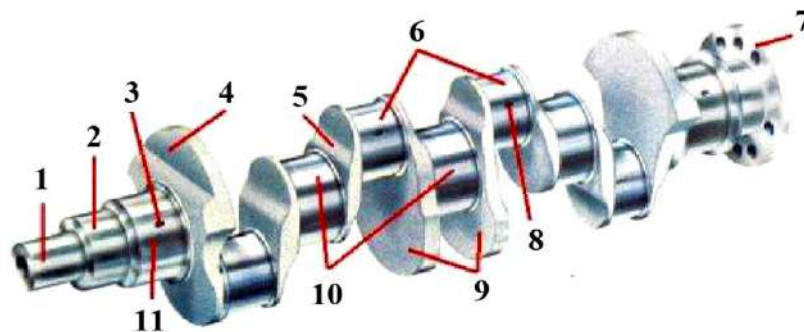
Конструкция коленчатого вала: 1 – носок; 2 – посадочное место шестерни привода распределительного вала; 3 – отверстие для подвода масла; 4 – противовес; 5 – щека; 6 – шатунные шейки; 7 – фланец маховика; 8 – отверстие для подвода масла; 9 – противовесы; 10 – коренные шейки; 11 – коренная шейка упорного подшипника [58]
